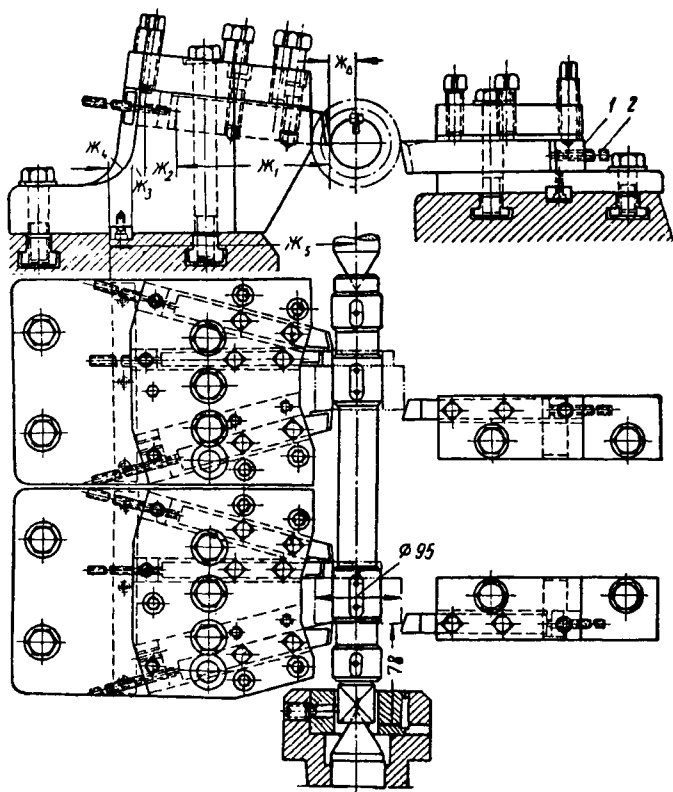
Схема настройки токарного многолезцового полуавтомата, снабженного регулируемыми опорами 1 и винтами 2 для установки резцов
